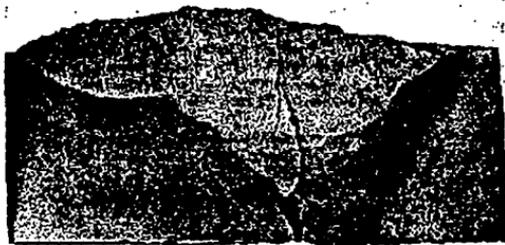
Falta de penetración en la raíz de una soldadura a tope que condujo a la ruptura del tubo de acero al carbono para alimentación de agua de una caldera por agrietamiento debido a esfuerzos de corrosión.
